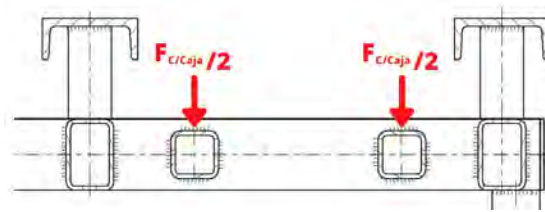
DCL de las fuerzas que se aplican a la unión soldada.
